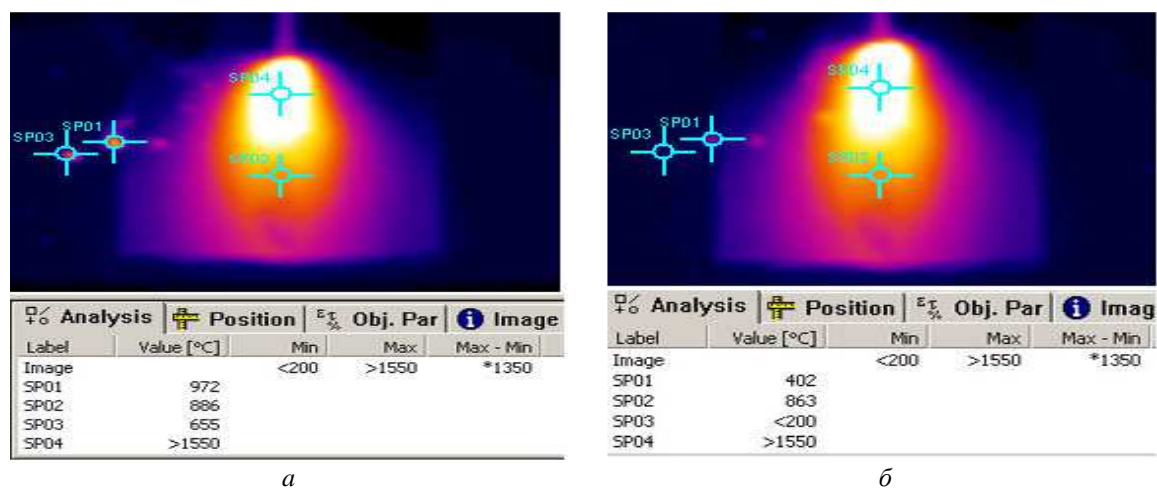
Тепловизионные кадры ручной дуговой сварки покрытыми электродами при попадании каплей-брызг расплавленного металла на поверхность свариваемых изделий:
